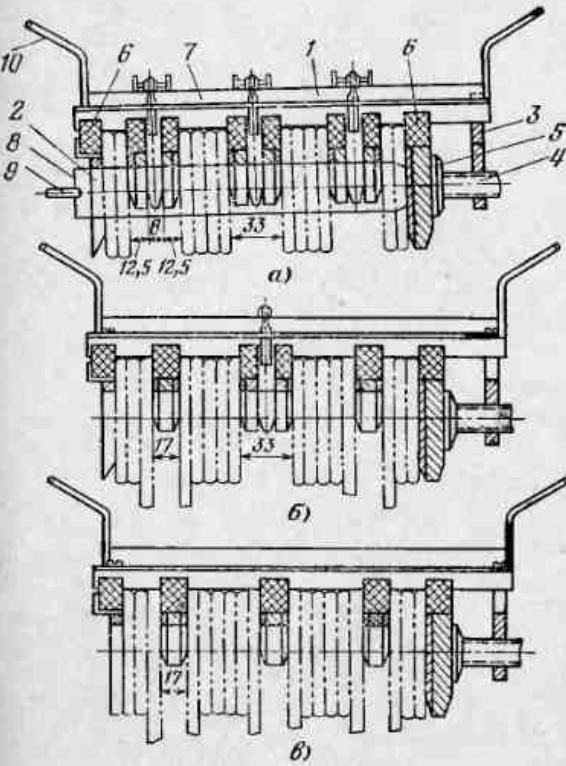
Комплект кондукторов для сварки прямых ответвительных и тройниковых секций ШМА.
